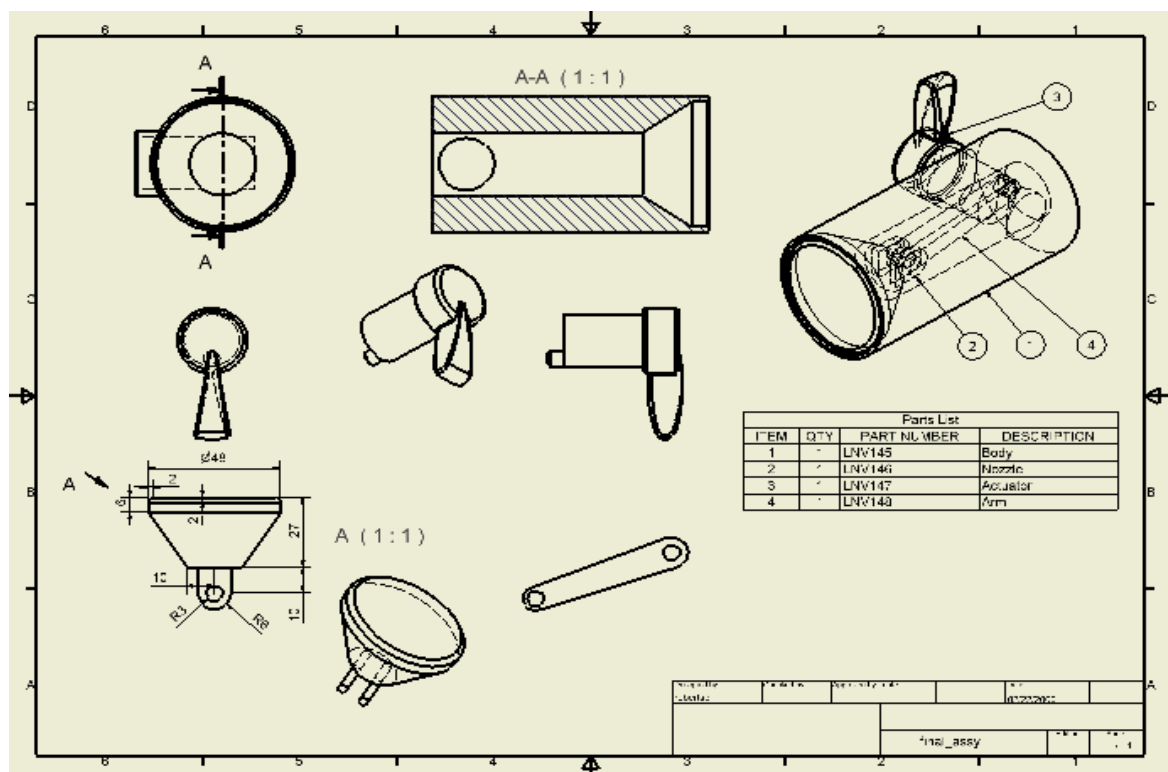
Dibujo de detalle, configuración de partes y componentes.
